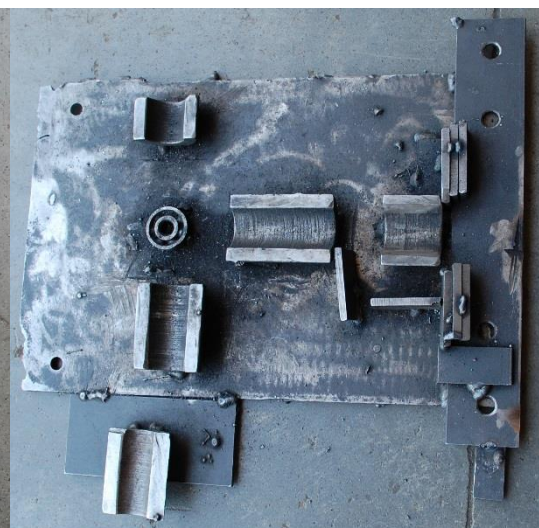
Svařovací přípravek 1456-90-ROT
